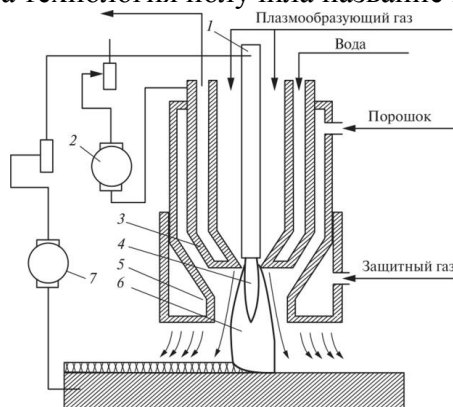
Установка для плазменной наплавки с вдуванием порошка в сварочную дугу:
